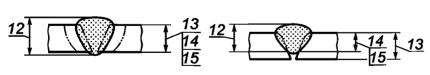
Примеры швов при сварке плавлением Figure 12 — Typical examples of fusion welds Figure 12 — Exemples types de soudures par fusion
